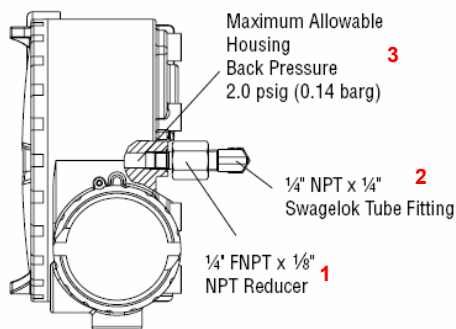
Штуцер сброса газа из главного корпуса позиционера
